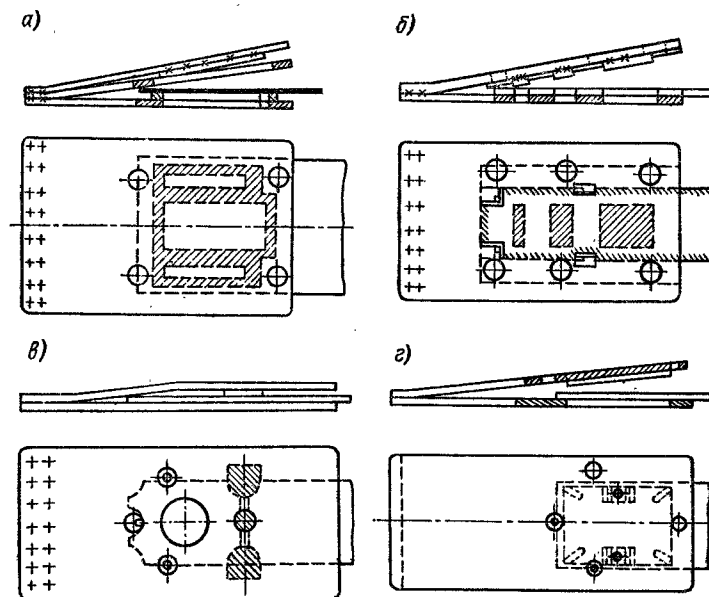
Конструкции листовых «пинцетных» штампов; а — для вырезки и пробивки; б — для пробивки; в — для отрезки; г — для вырезки
